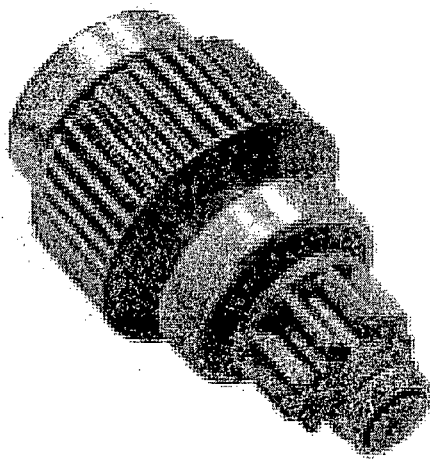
Impulsionador de um motor de partida do tipo com redução.
